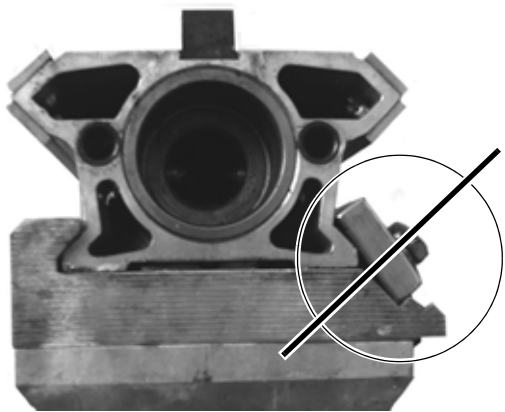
Направляющий рельс закреплен на поворотной колодке неправильно
